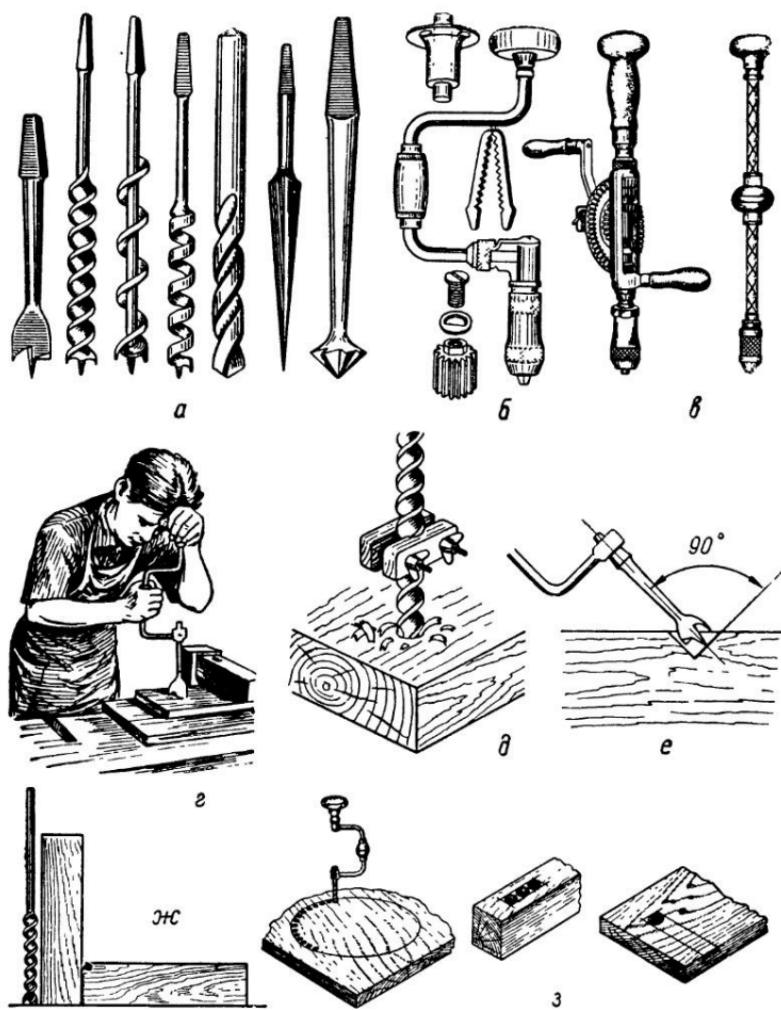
Сверлильные инструменты: а — сверла: перка центровая (слева), винтовые сверла, спиральное сверло, шиловое сверло и зенковка; б — коловорот и его части; в — дрели; г — прием сверления коловоротом; д — самодельный ограничитель глубины сверления; е — сверление под углом к плоскости; ж — проверка направления сверла по угольнику; з — сверление как вспомогательная операция при изготовлении больших отверстий и долблении.
